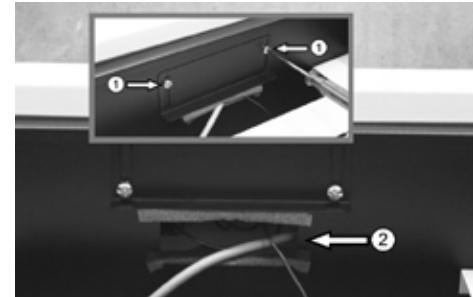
Kabeldurchführung ② am Schaltfeldgehäuse
